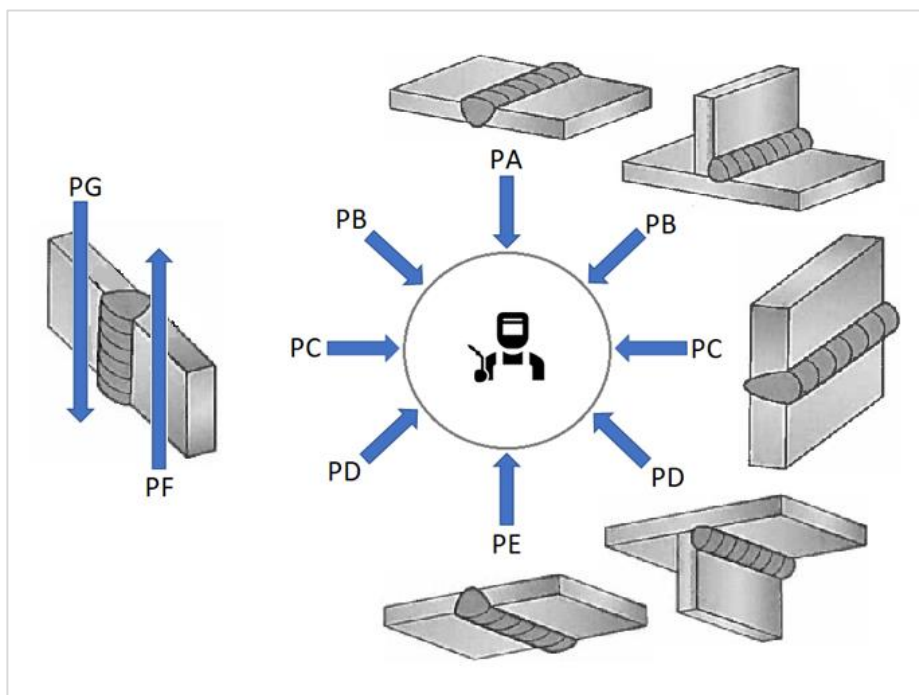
Posições de soldadura segundo EN ISO 6947 - [10] Imagem adaptada
